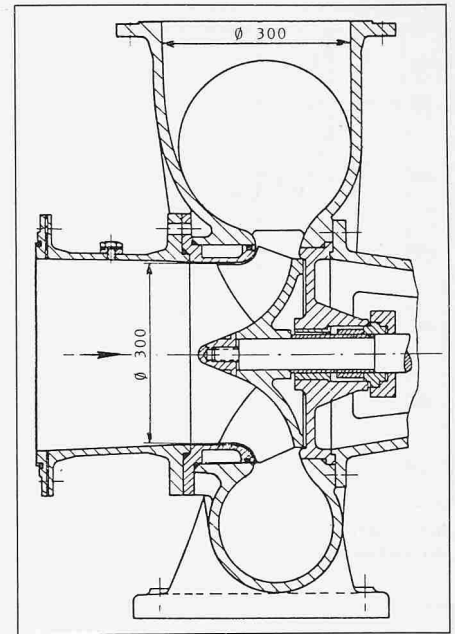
Schnittbild der Versuchspumpe mit halbaxialem Laufrad.
